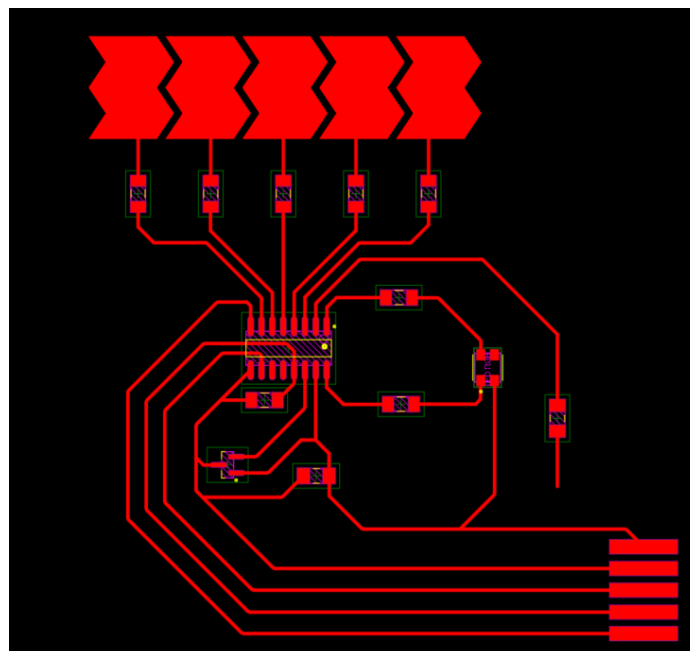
Diseño PCB con grosor de pista de 0,5mm
